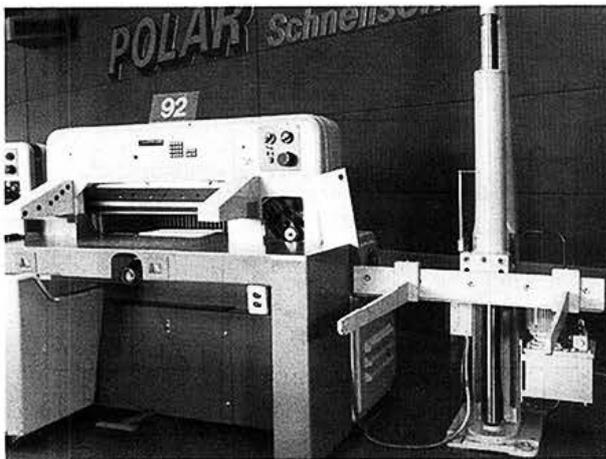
Stapellift mit hydraulischem Antrieb
